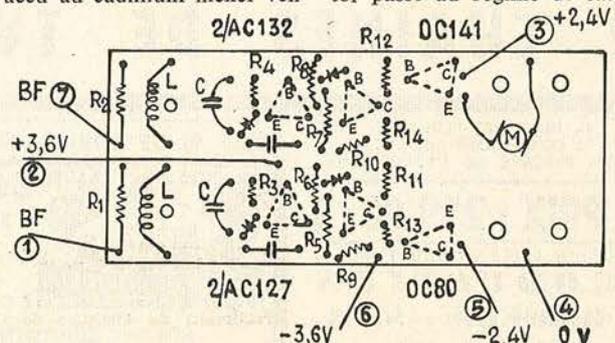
Disposition des pièces du servo n° 2. Vue du côté bakélite
